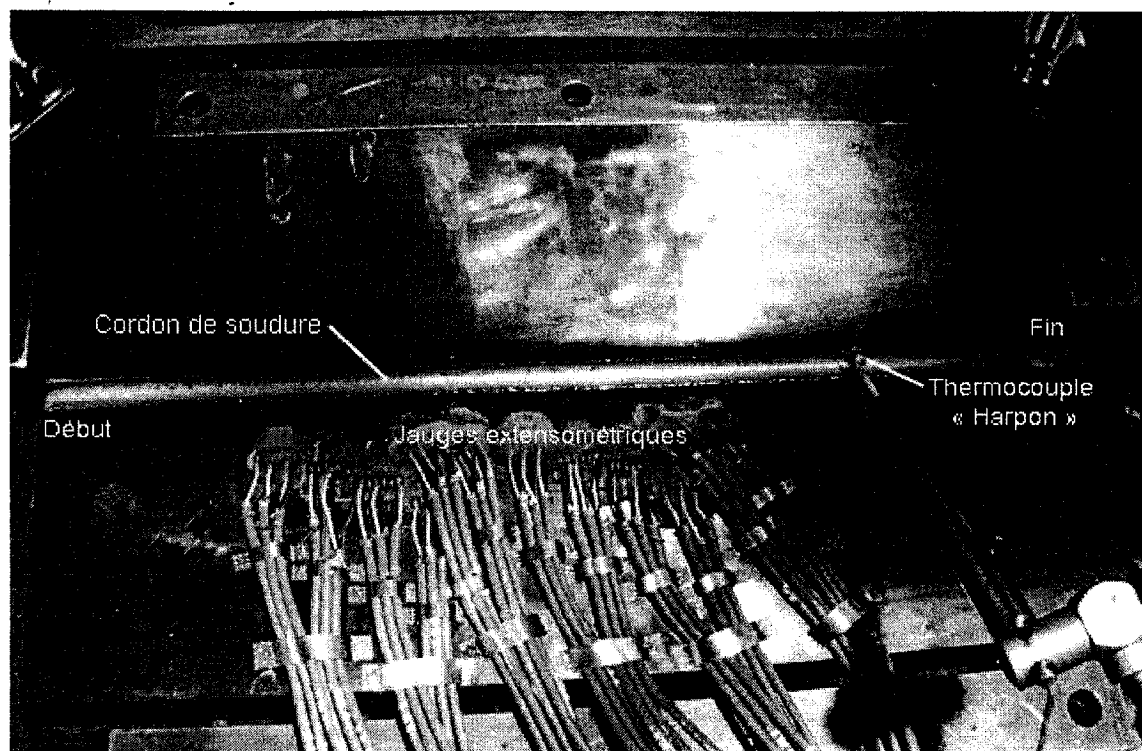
Vue d'ensemble de la plaque d'acier ASTM A516 après le passage de l'arc
